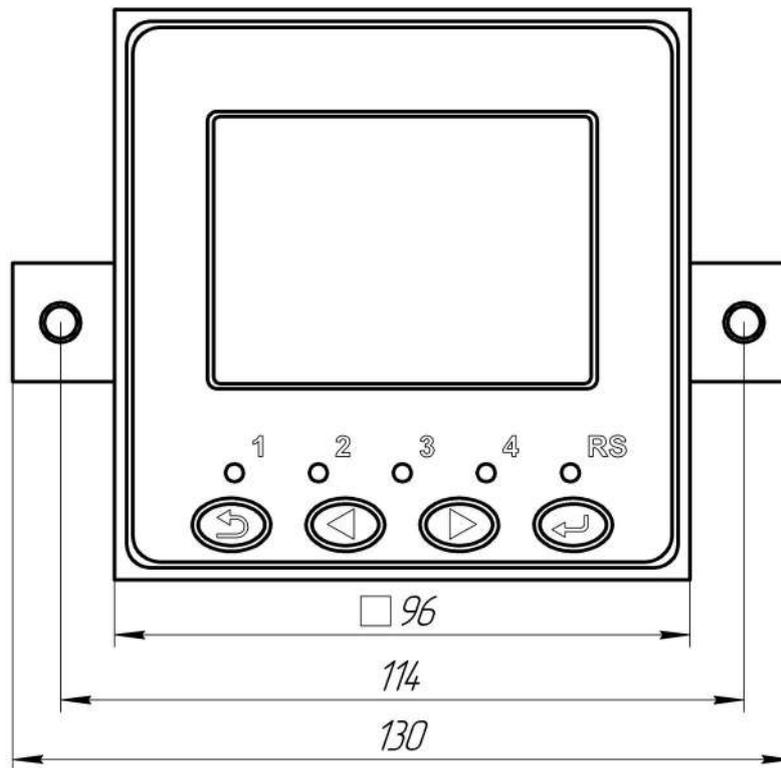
Габаритные размеры контроллера щитового исполнения
